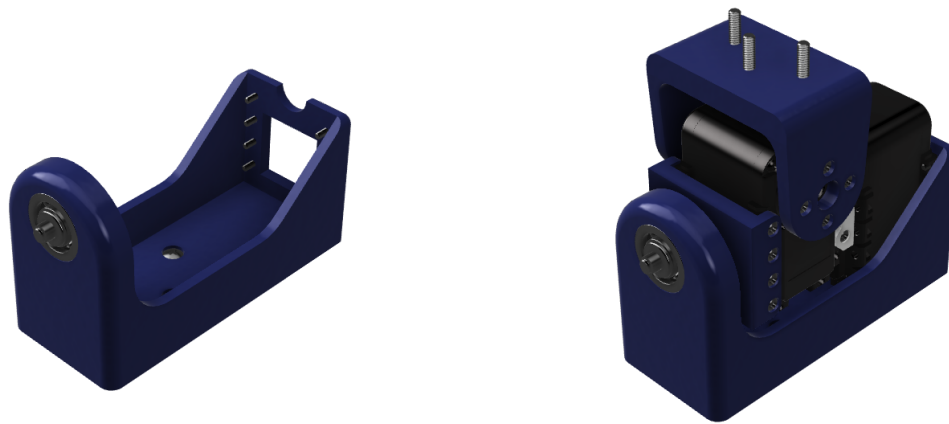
a) Base para los servomotores (izquierda), b) ensamble de la muñeca (derecha).
